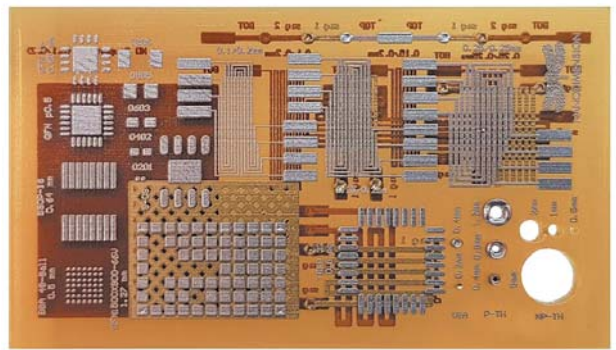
Внешний вид ПМП, изготовленного на 3D-принтере
